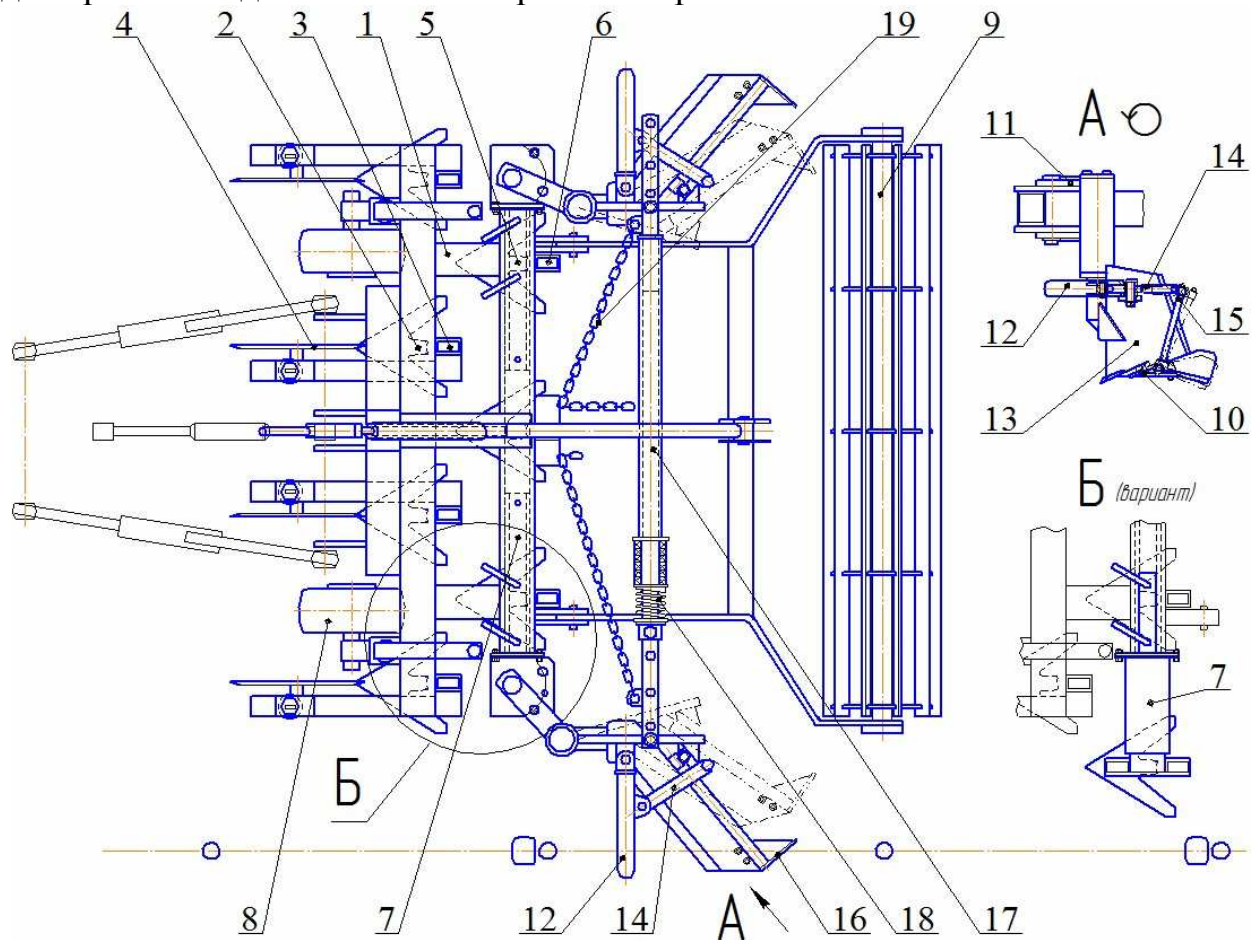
Схема культиватора междустовой обработки виноградников, вид сверху с консольно-пальцевым креплением дополнительных боковых рабочих органов: с поворотной лапой – вид А или варианта со стрельчатой лапой – вид Б
